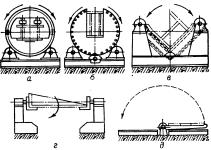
Кантователи: a — роликовый; b — цевочный; b — цепной; b — цапфовый; d — рычажный.
